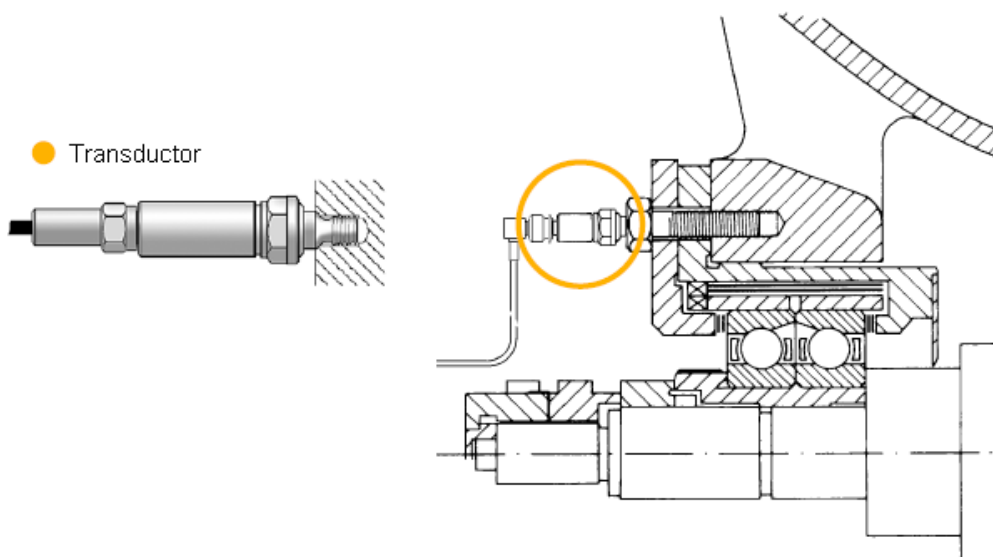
Transductor próximo al cojinete del lado del compresor o de la turbina.
